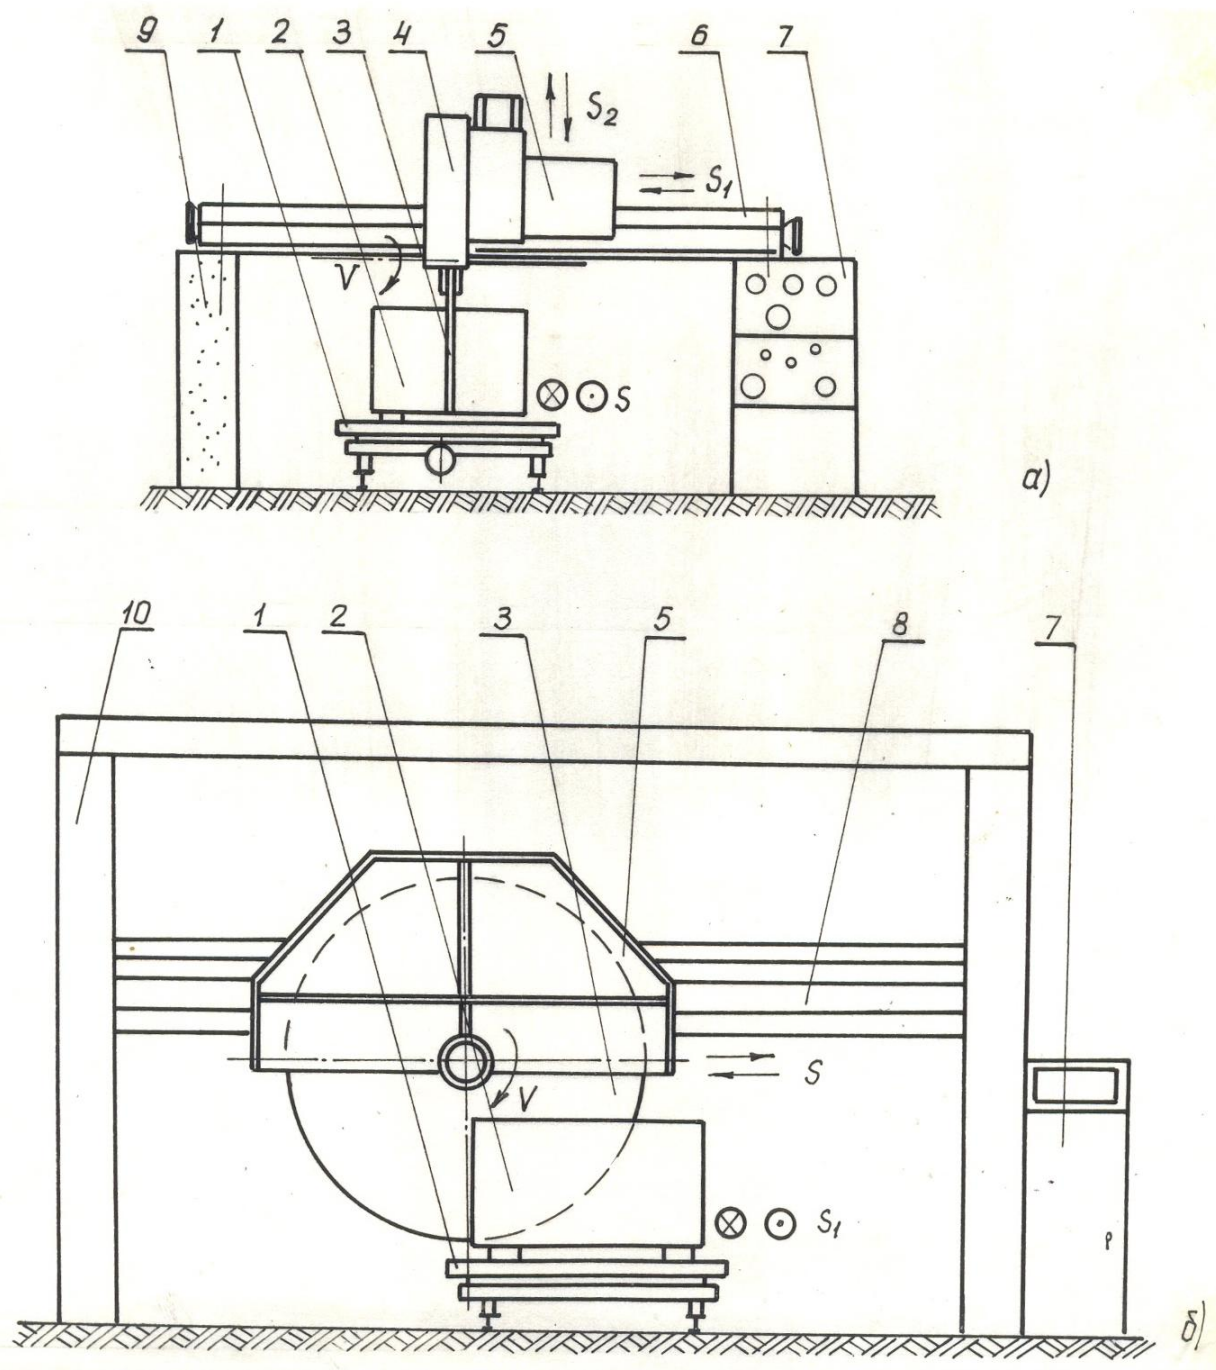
Схема компоновки мостового (а) и порталного (б) отрезных станков с отрезным кругом гигантом. 1 – тележка для установки блока; 2 – распиливаемый блок; 3 – алмазный отрезной круг; 4 – защитный кожух круга; 5 – суппорт; 6 – направляющая траверса портала; 7 – пульт управления; 8 – мост; 9 – железобетонные опоры моста; 10 – колонны портала.  $V$  – скорость вращения (резания) круга;  $S$  – рабочая подача;  $S_1$  – установочное перемещение блока (б) или отрезного круга (а).
